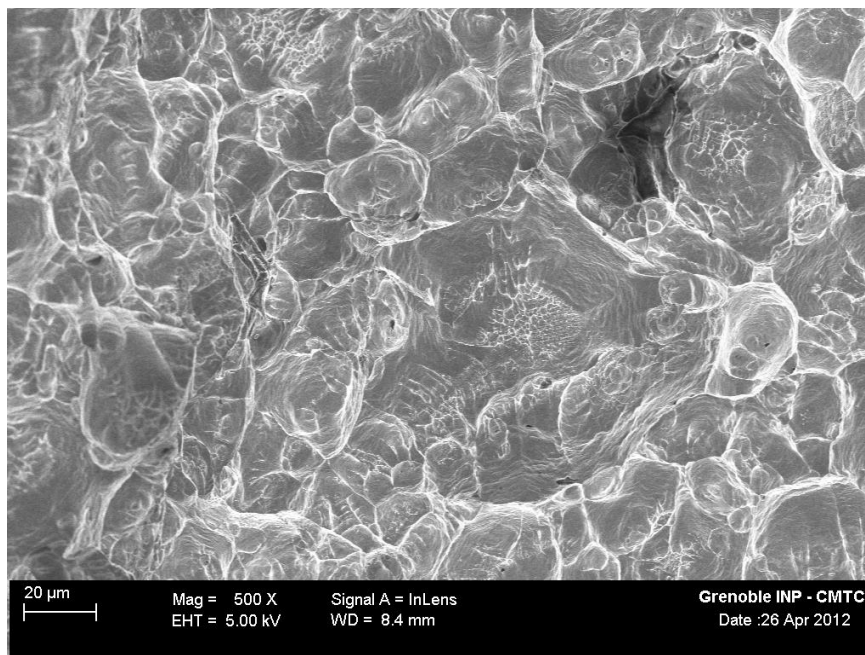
Fractografía de la probeta cilíndrica ASTM con entalle en 90°, de cátodo. En la imagen de SEM, se muestra un aumento de x500 de la zona de fractura.
